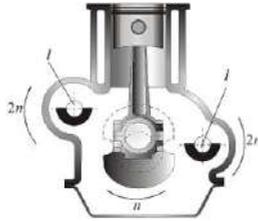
Установка балансирних валів рядного чотирициліндрового двигуна:
